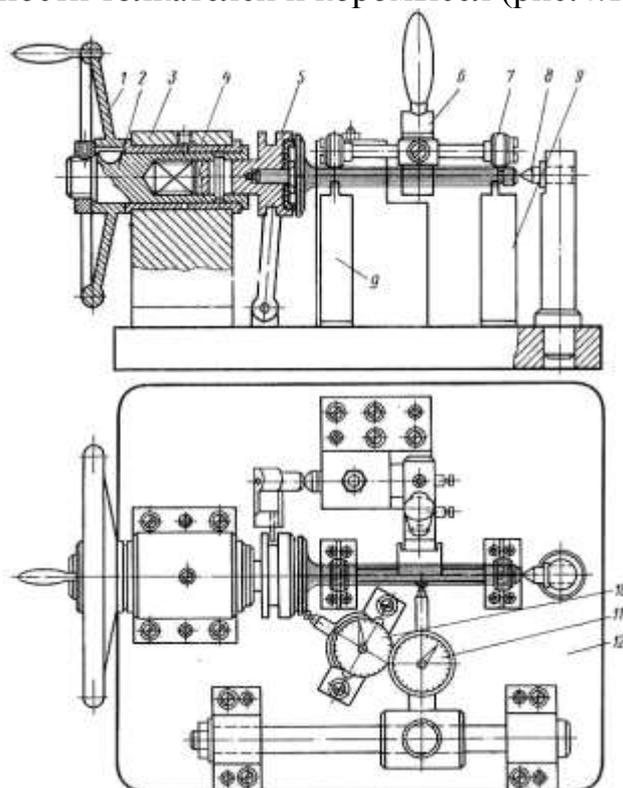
Приспособление для расточки и проверки клапана: 1-маховик; 2-валик; 3-стойка; 4-втулка; 5-палец; 6-кронштейн; 7-ролик; 8-центр; 9-призма; 10, 11-индикаторы; 12-плита.
